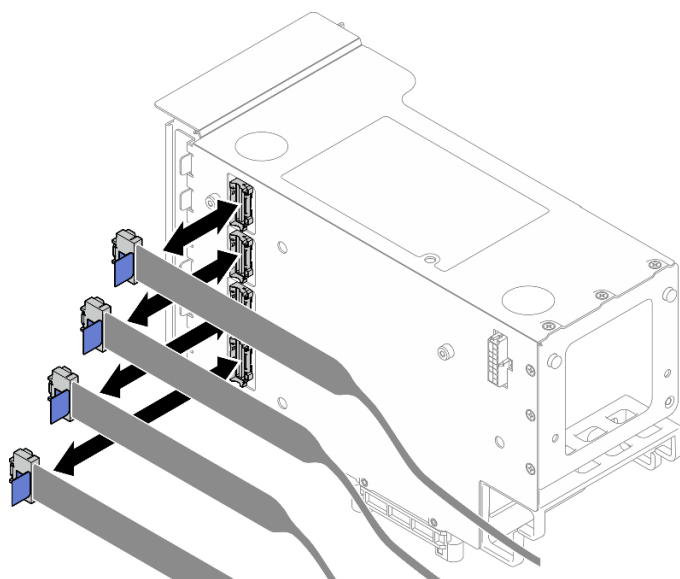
Desconectando cabos PCIe do exterior da placa riser
